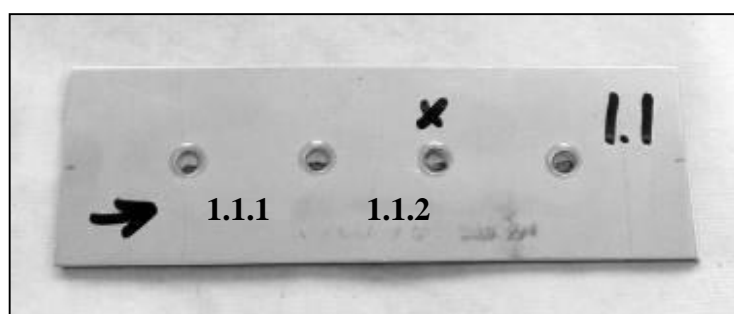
Внешний вид точечной контактной сварки образца № 1.1
